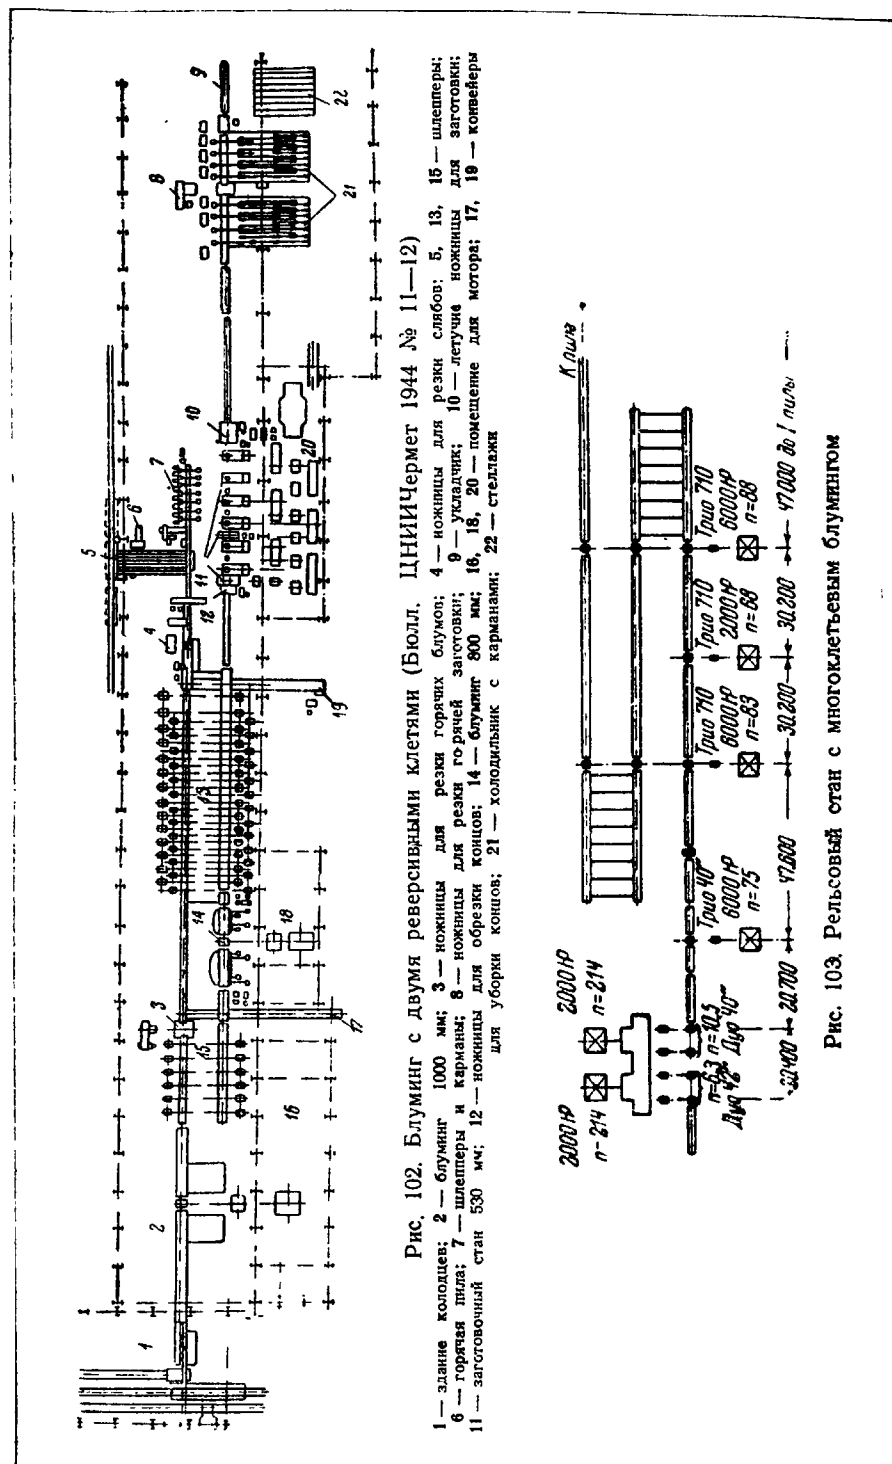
Блуминг с двумя реверсивными клетями (Бюлл. ЦНИИЧермет 1944 № 11—12)
